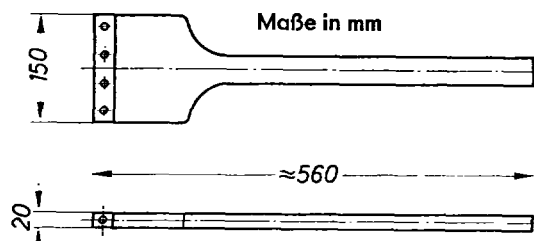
Stampfer für Biegekörper, Gewicht: 0,675 bis 0,720 kg
